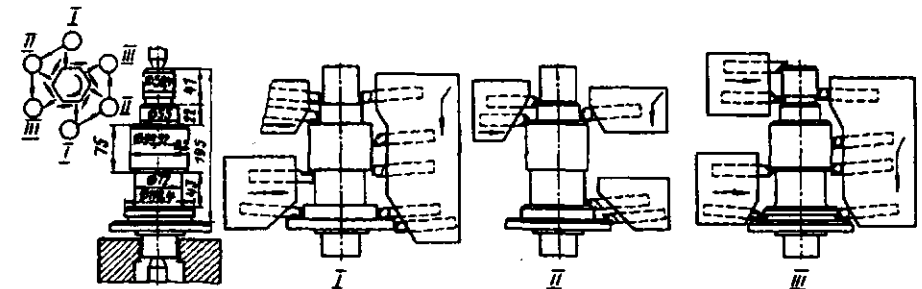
Наладка шестишпиндельного полуавтомата непрерывного действия для трехциклового обработки заготовок шестерен
